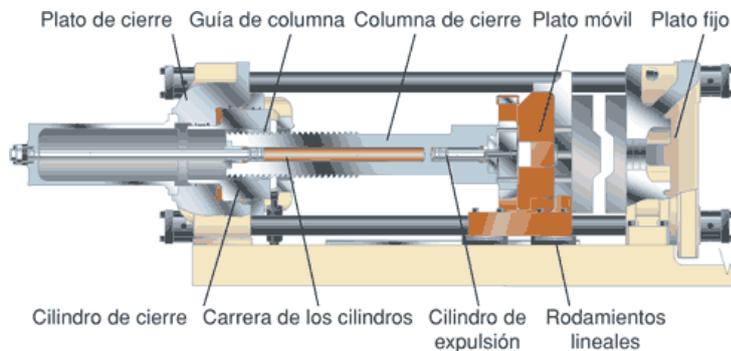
Sistema de cierre hidráulico de la máquina de inyección
